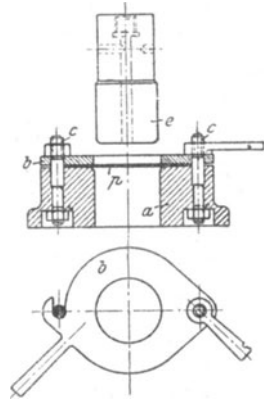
Ziehwerkzeug mit schwenkbaren Platte als Niederhalter. a Ziehring, b Niederhalter, c Spannschraube und Bolzenschraube für b, e Stempel, p Blechscheibe.
